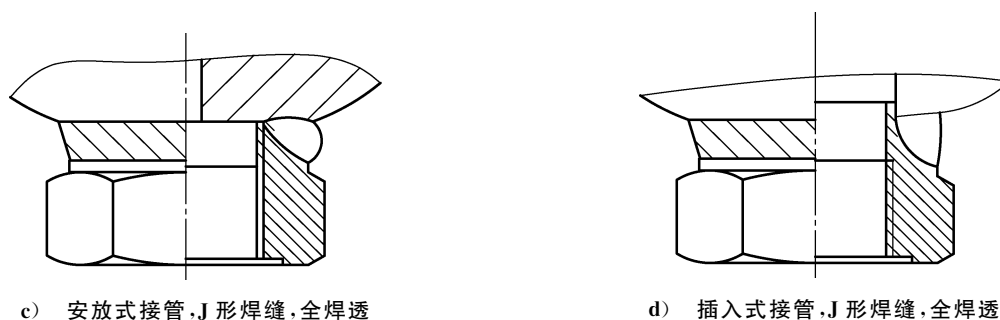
充气端和液端接头的典型焊接接头形式 (续)
